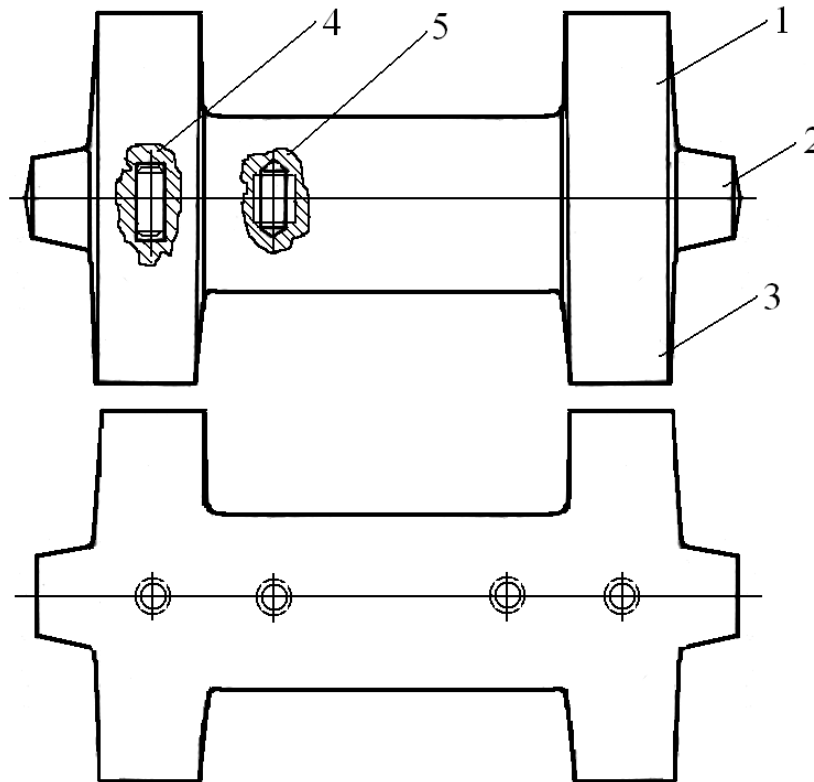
Модель виливка, що показаний на рис. 1. 1 – модель верхньої частини; 2 – стержневий знак; 3 – модель нижньої частини; 4 – центрувальний штифт; 5 – різьбові отвори
